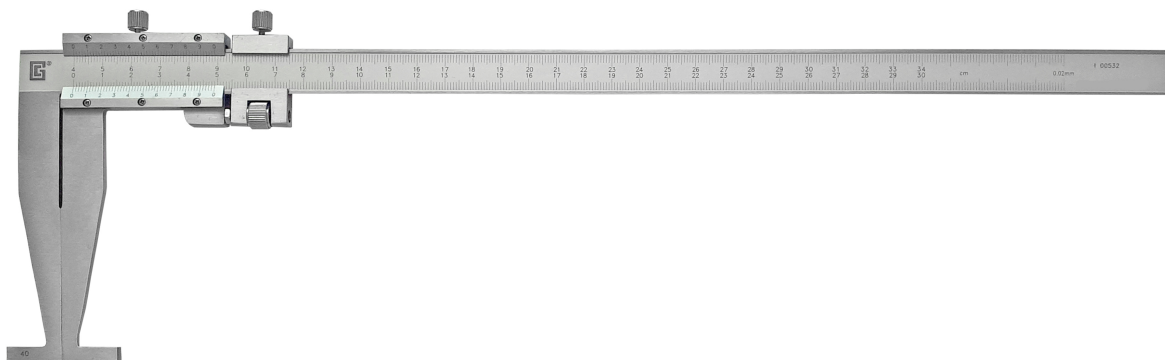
Общий вид штангенциркулей модели ШЦС-115, тип А
